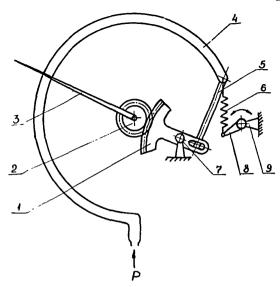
Кинематическая схема прибора: I — сектор; 2 — трибка; 3 — стрелка; 4 — трубчатая пружина; 5 — тяга; 6 — пружина корректора; 7 — ось сектора; 8 — эксцентрик корректора; 9 — корректор нуля; Р — измеряемое давление
